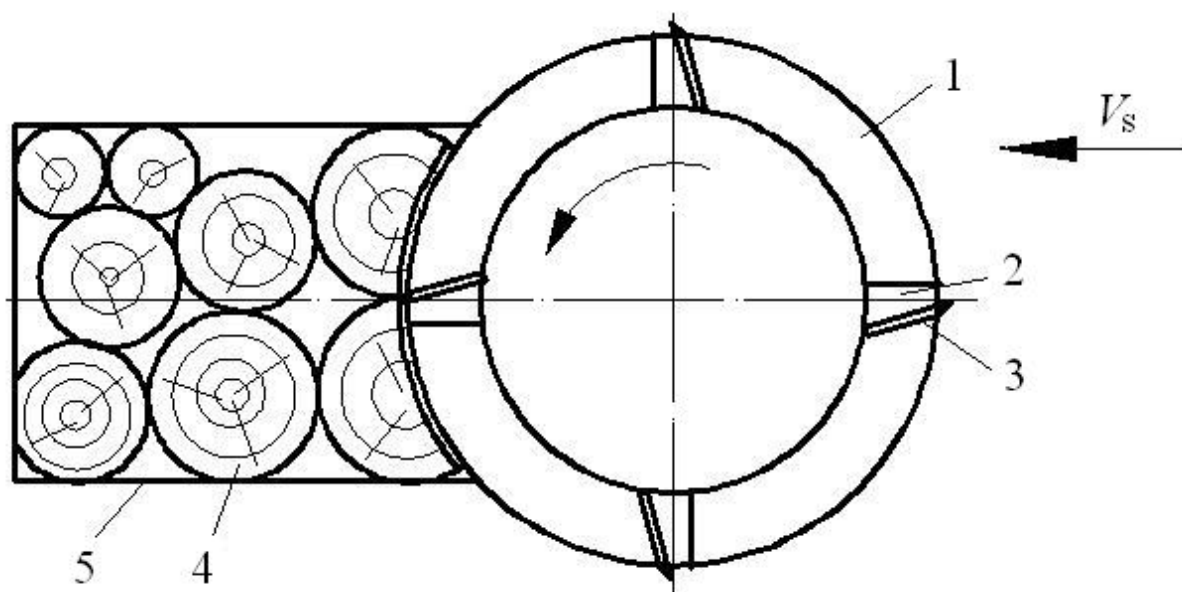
Схема цилиндрического поперечного фрезерования барабаном с ножами на внешней поверхности:
